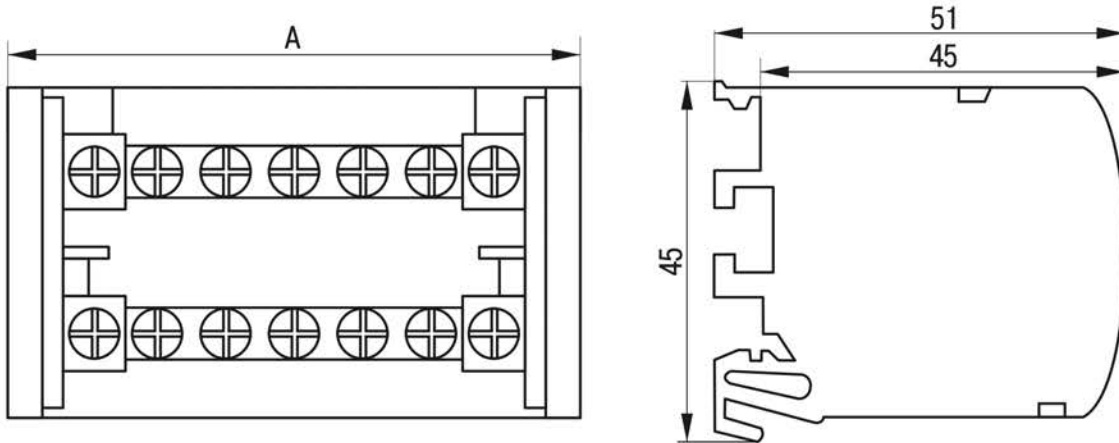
Габаритные размеры шин ШНК 2×7, ШНК 2×11 и ШНК 2×15 /
